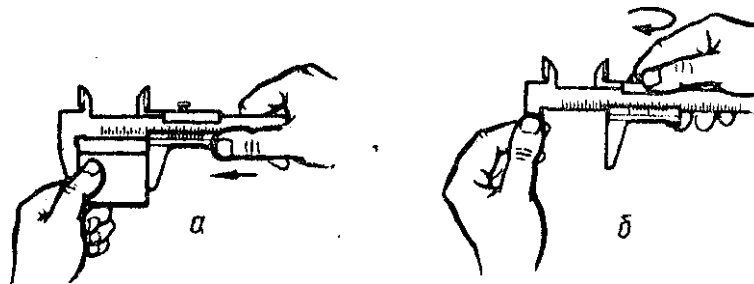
Прийом вимірювання штангенциркулем ШЦ-І:
